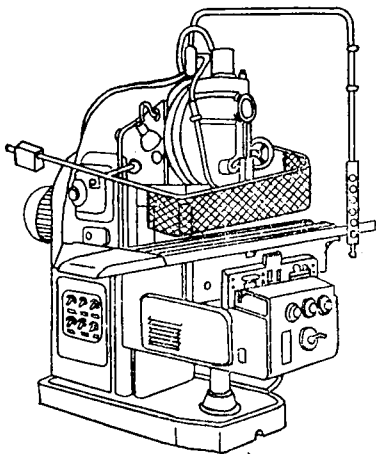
Защитное приспособление для вертикально-фрезерного станка.
